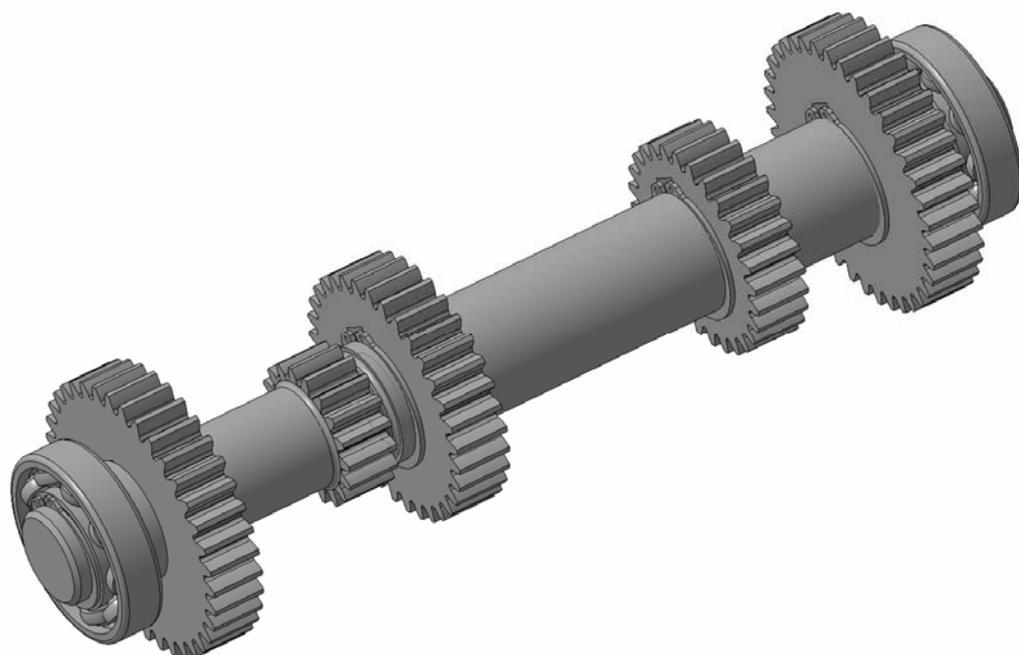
Модель собранного вала с полным комплектом зубчатых колес и подшипников
